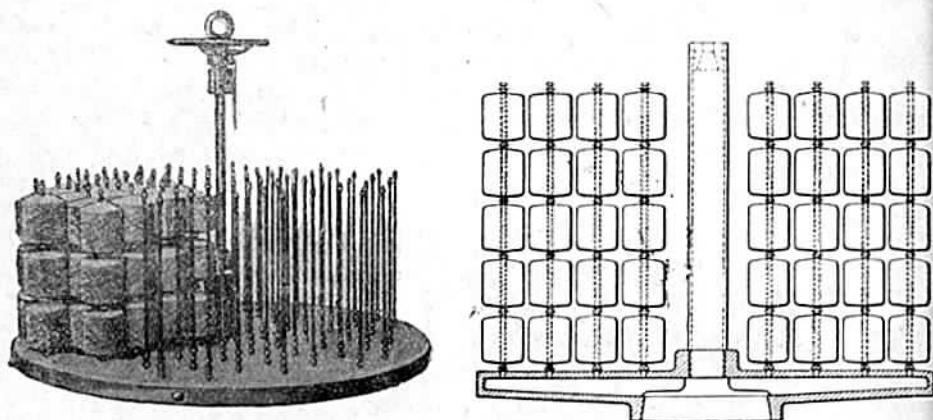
Общий вид и схематический разрез каретки для насаживания крестовых шпул.
